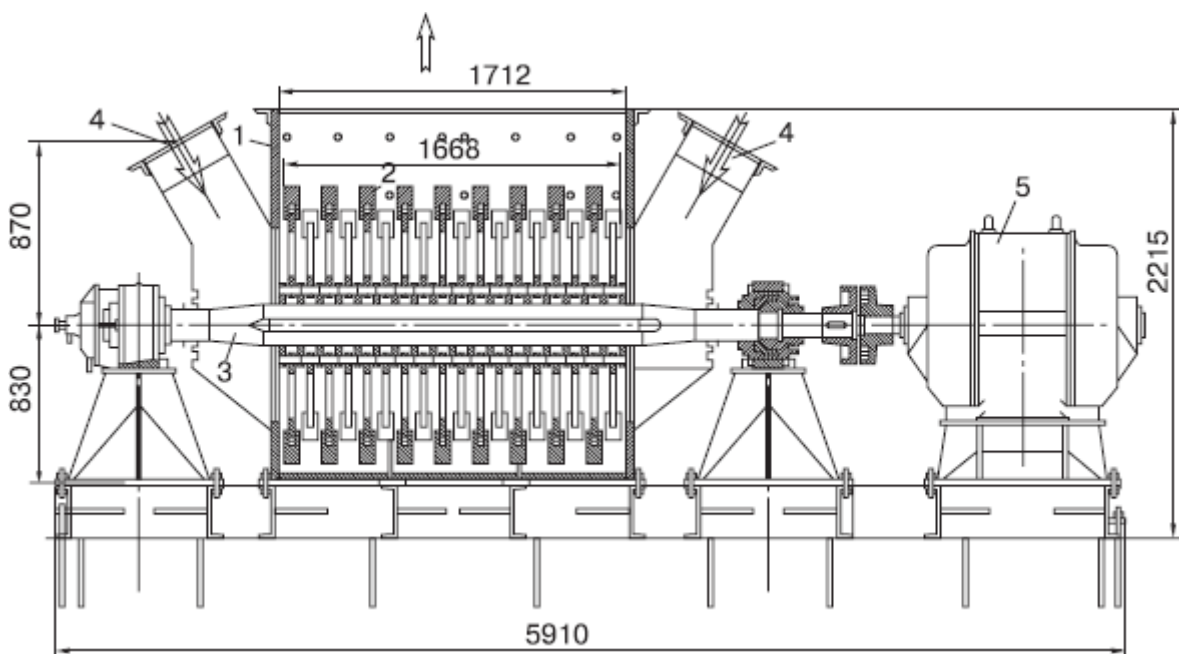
Молотковая мельница с аксиальным подводом сушильного агента: 1 – корпус; 2 – била; 3 – ротор; 4 – патрубки для подвода сушильного агента; 5 – электродвигатель
